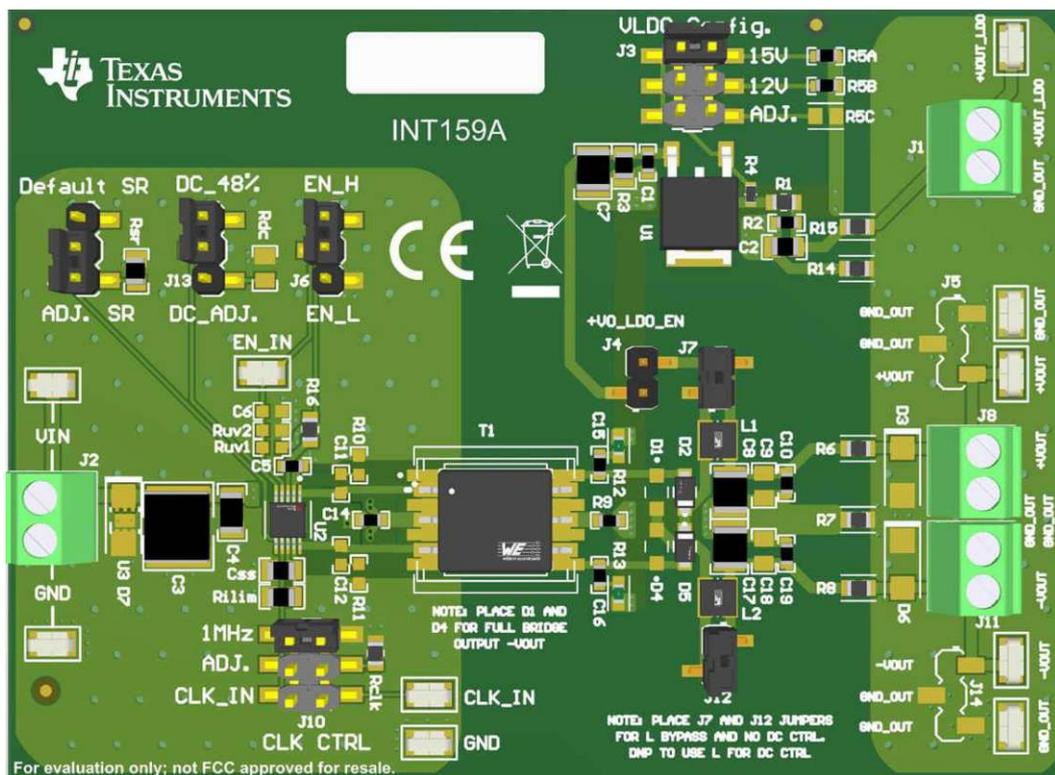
PCB 3D Ansicht SN6507DGQEVMB
